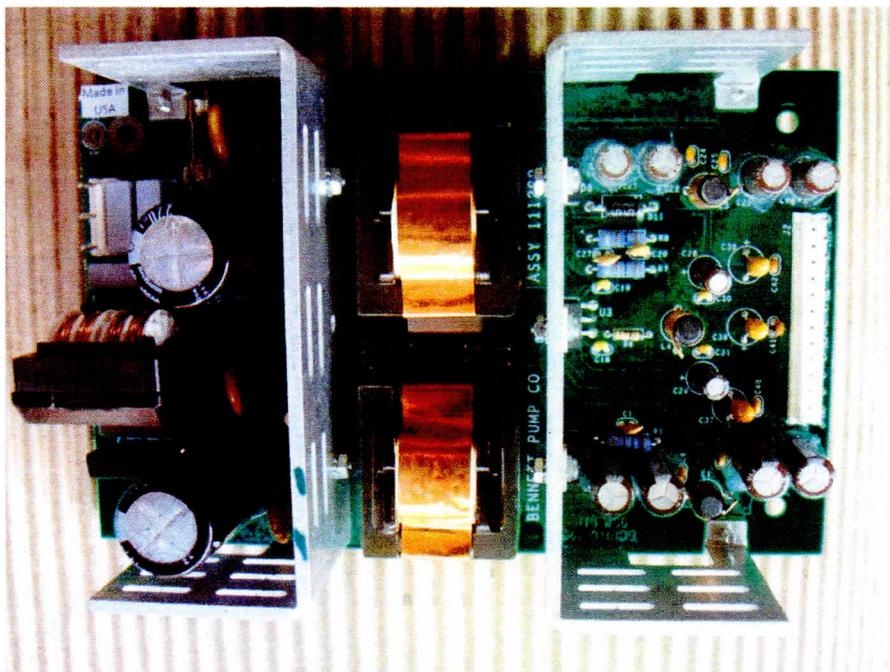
Tarjeta del módulo POWER SUPPLY ASSEMBLY identificada con número de parte 111209 revisión J, vista cara componentes.
